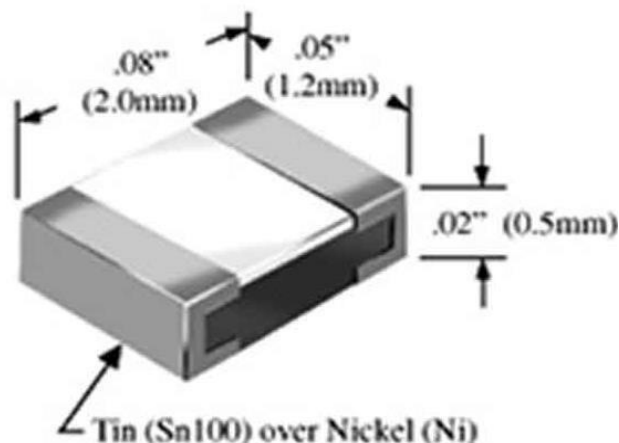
Габаритні розміри і вигляд резистора RC0805
